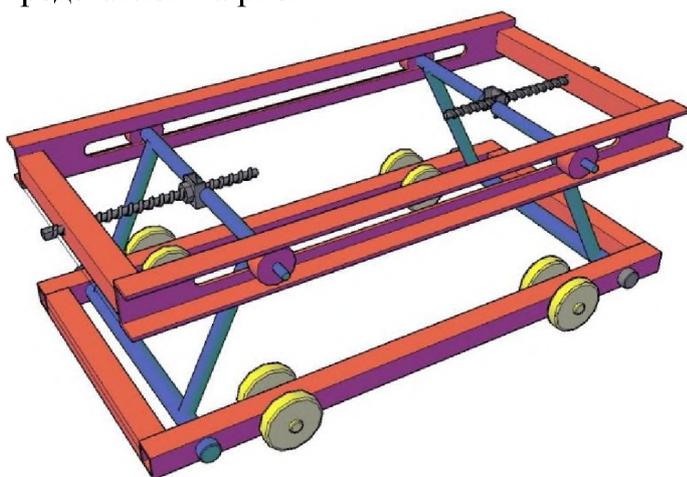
Конструкция подкатного лежака с регулируемой высотой подъема
